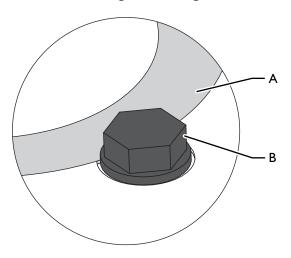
Exzenterring blockieren: Sechskantschraube
